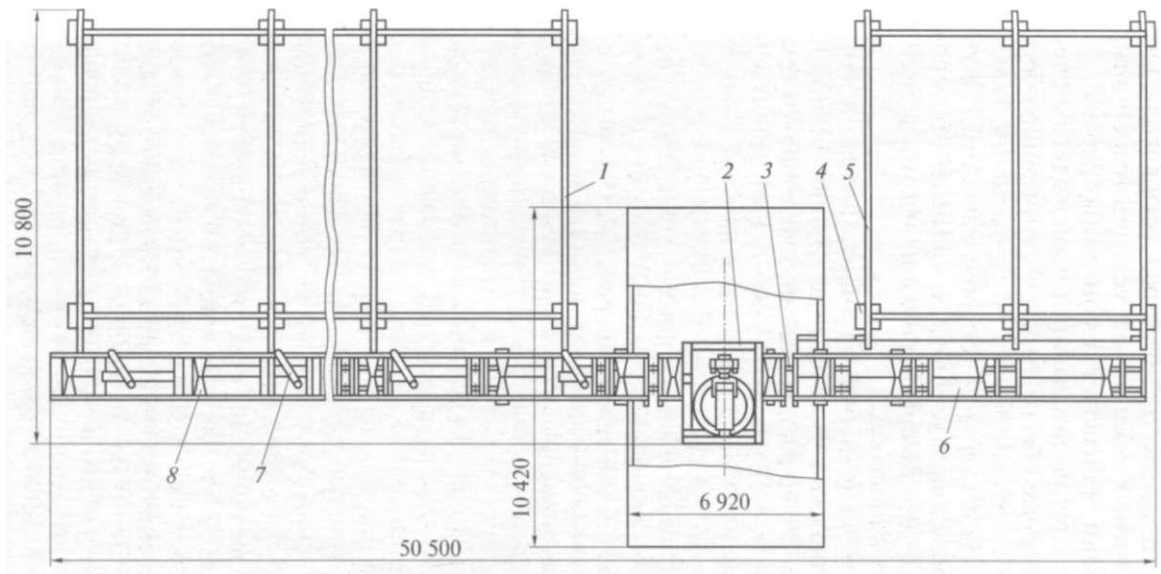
Схема стационарной установки УСТ-630 для сборки и сварки секций трубопроводов с $D = 80 \dots 600$ мм:
